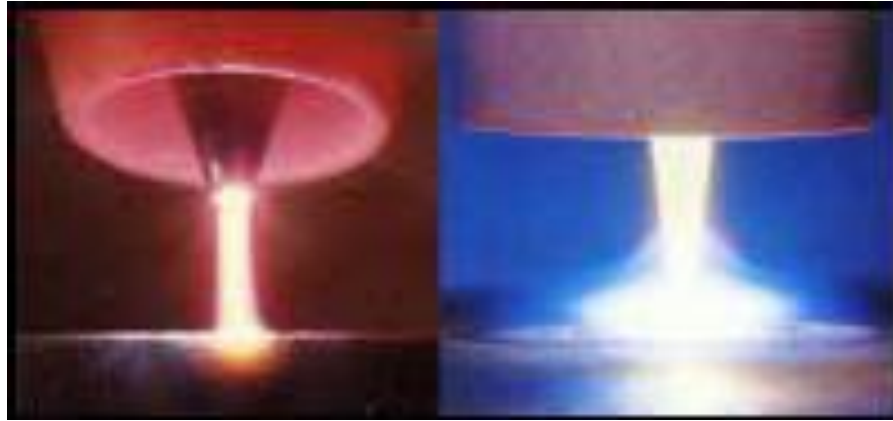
Foto comparativa entre de soldadura por plasma (izquierda) y soldadura TIG (derecha)
